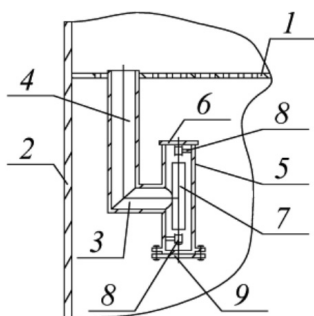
Переливное устройство статического типа [9]: 1 – полотно тарелки; 2 – стенка колонны; 3 – переливное устройство; 4 – патрубок для слива жидкости с тарелки; 5 – патрубок для выхода жидкости из перелива; 6 – клапан; 7 – поплавок; 8 – тяга; 9 – заглушка
